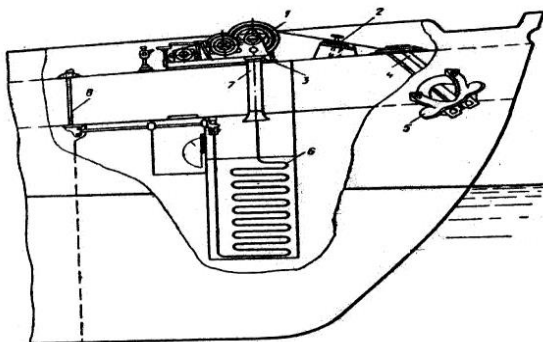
Схема якорного устройства [11]. 1 – брашпиль; 2 – стопор; 3 – палубный клюз; 4 – якорный клюз; 5 – якорь; 6 – якорь-цепь; 7 – межпалубный клюз; 8 – устройство для быстрой отдачи жвака-галса
